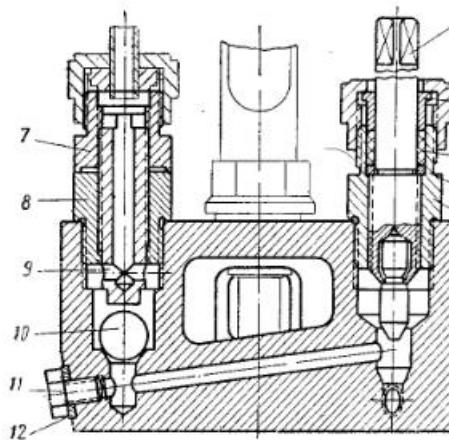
Газоотборный клапан двигателей типа NVD-24:
